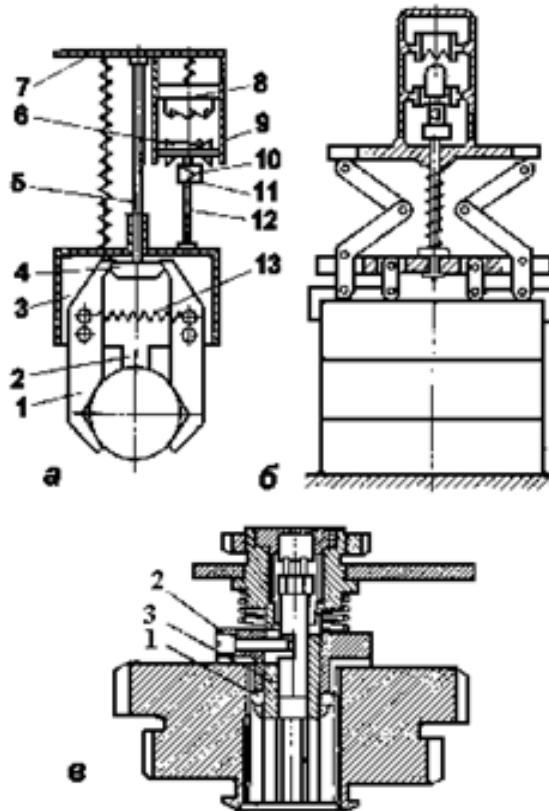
Не приводні захватні пристрої зі стопорними механізмами; а – для захоплення деталей по зовнішньому діаметру, б – для захоплення деталей, що лежать стопкою, в – для захоплення деталей по внутрішньому діаметру
